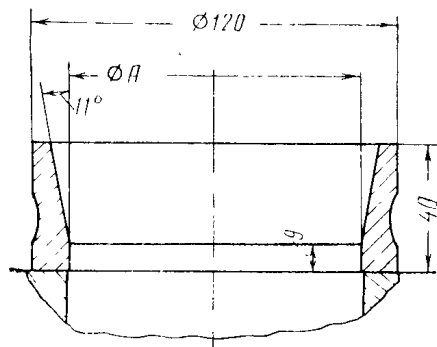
Приспособление для установки поршня с кольцами в цилиндр
